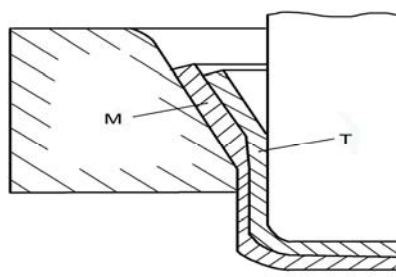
Схема комбинированной вытяжки двухслойной заготовки:
